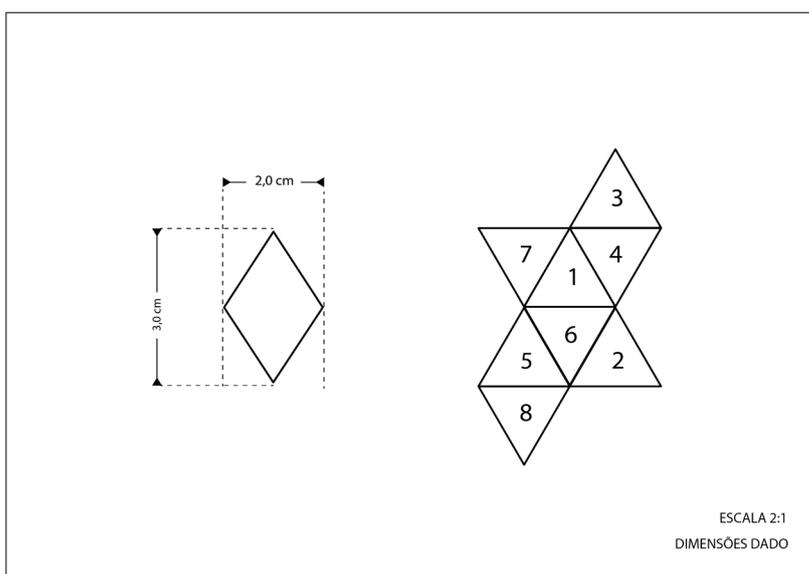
Vista frontal desenhada com dimensões do dado de 8 lados.
